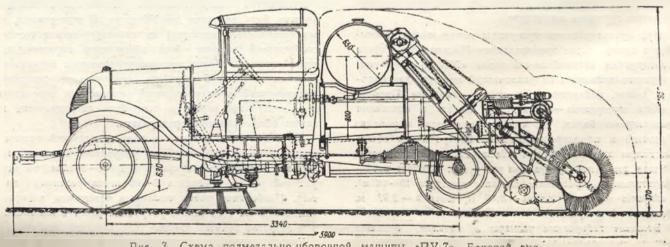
Схема подметально-уборочной машины «ПУ-7». Боховой вид
